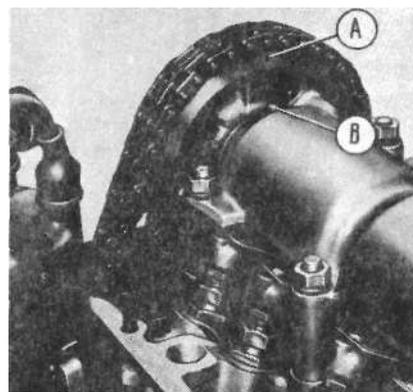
Установка поршня четвертого цилиндра в положение в. м. т. в конце хода сжатия по меткам на звездочке и корпусе распределительного вала
